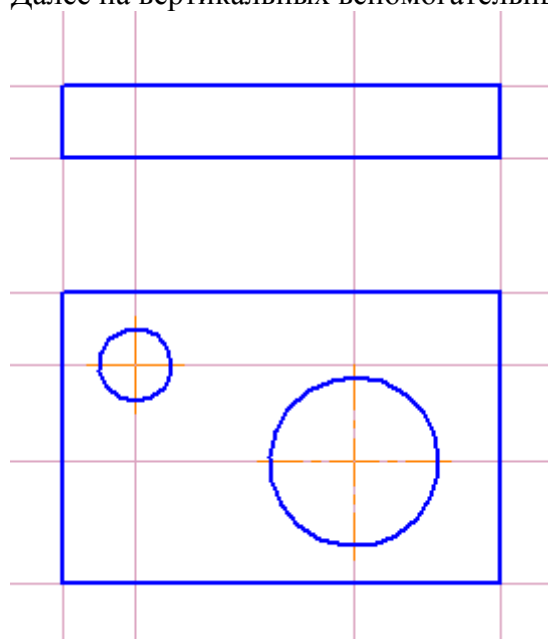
Фронтальный вид (без разреза) и вид сверху.
